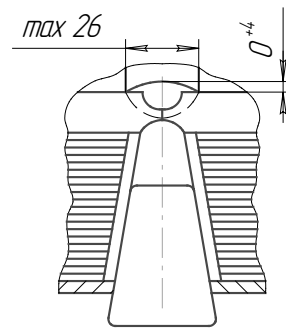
Контроль геометричних параметрів зварного з'єднання
